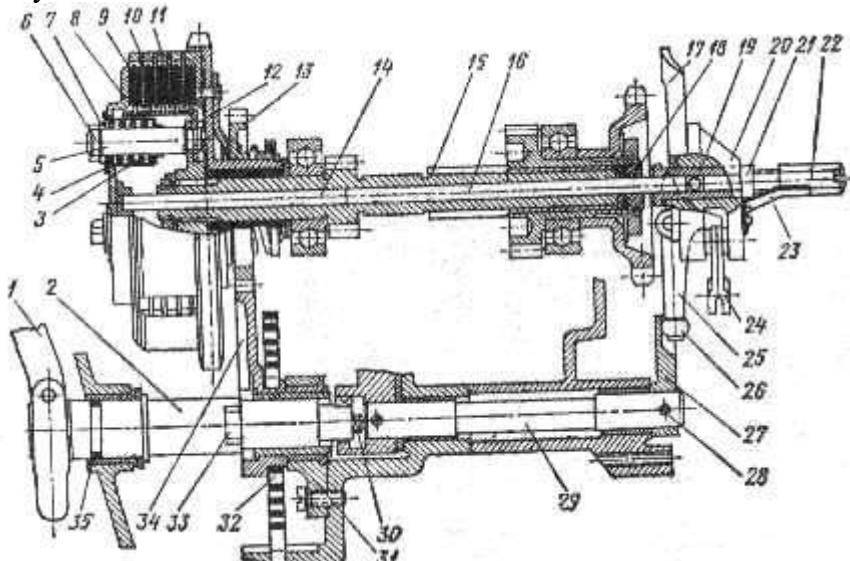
Разрез муфты сцепления, механизма выключения сцепления и пускового механизма моделей 353/04 и 354/04:
